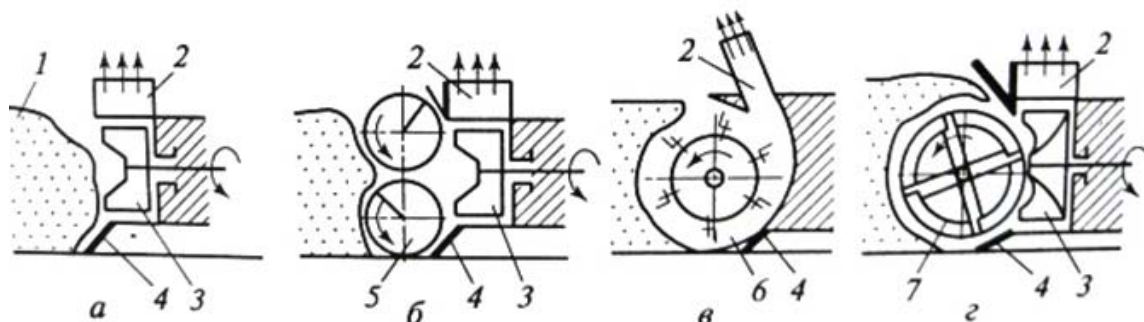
Типы рабочих органов роторных снегоочистителей: 1 – ротор; 2 – фрезерный барабан; 3 – направляющий патрубкок; 4 – плуг; 5 – шнек; 6 – фреза
